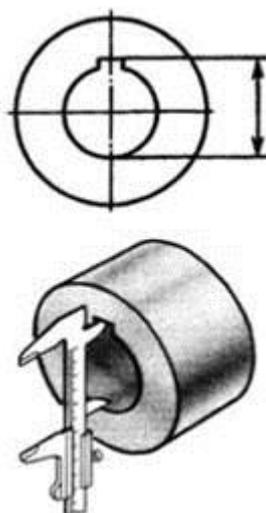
Нанесение размера глубины шпоночного паза, выполненного в отверстии
